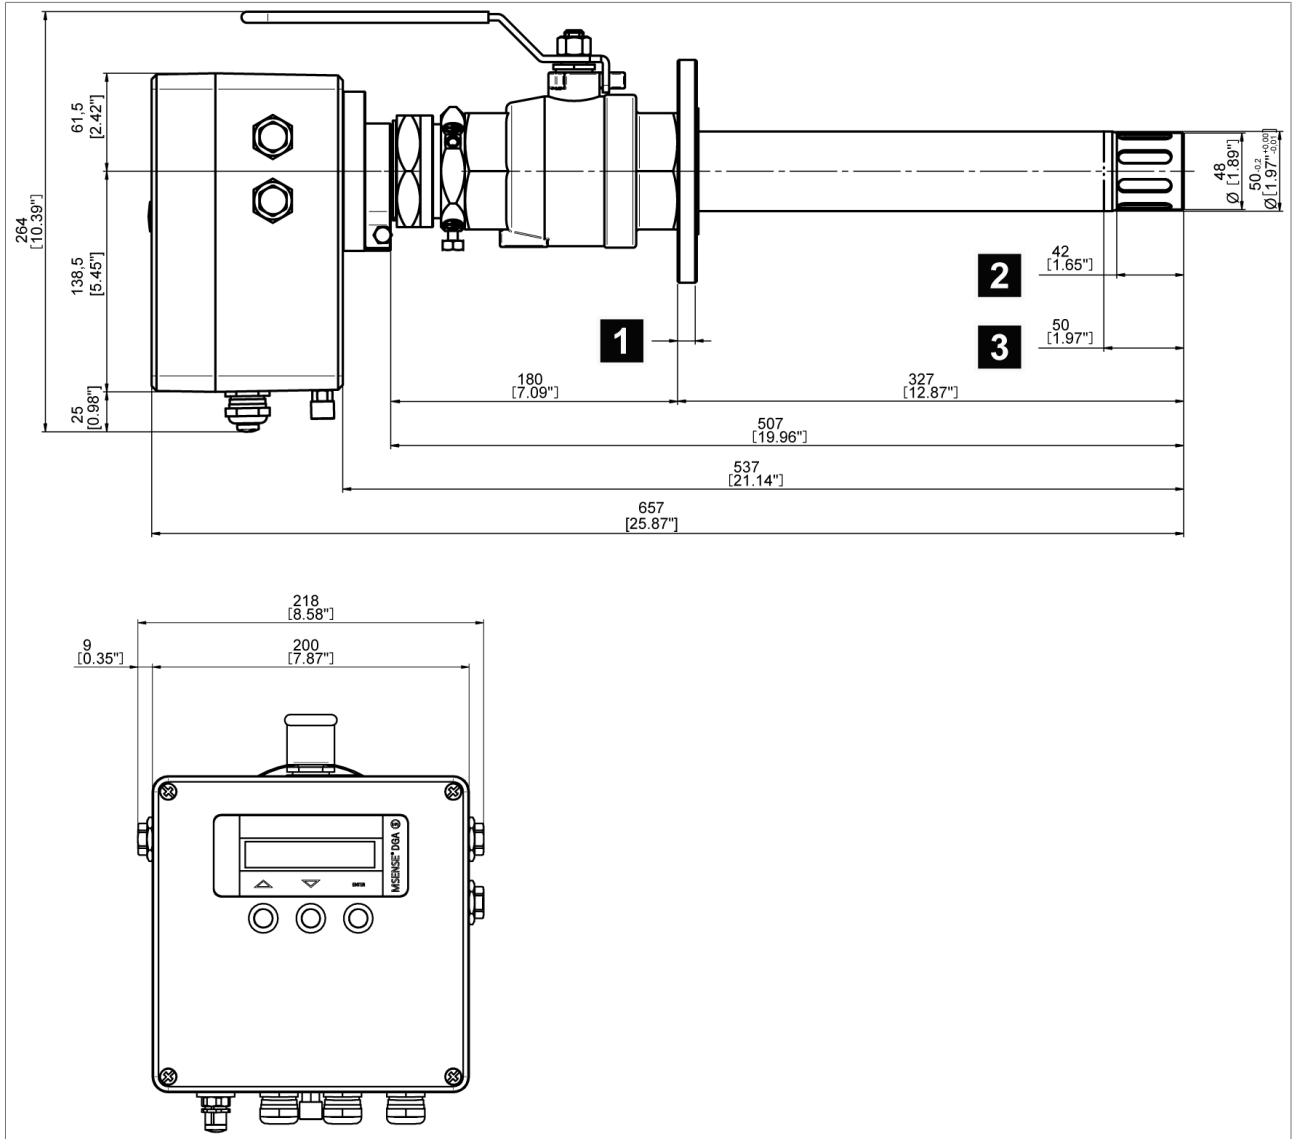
Dimensões do aparelho com tubo de medição com comprimento de 507 mm
